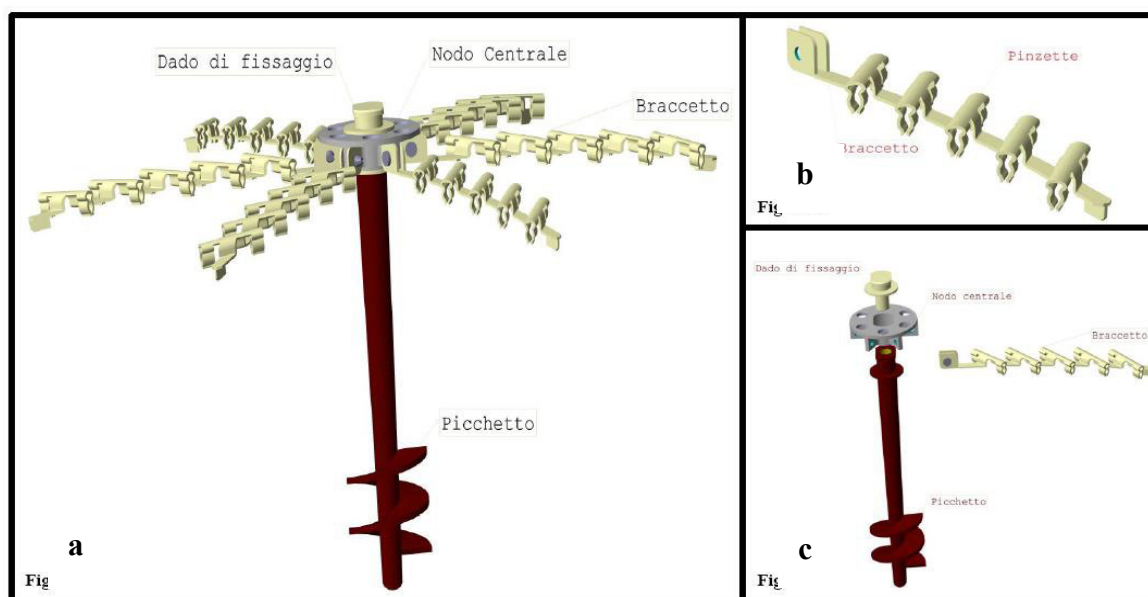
Supporto biodegradabile in Mater-Bi assemblato a raggiera (a) e particolari dei singoli moduli: braccetto (b) e picchetto con modalità di montaggio (c).
